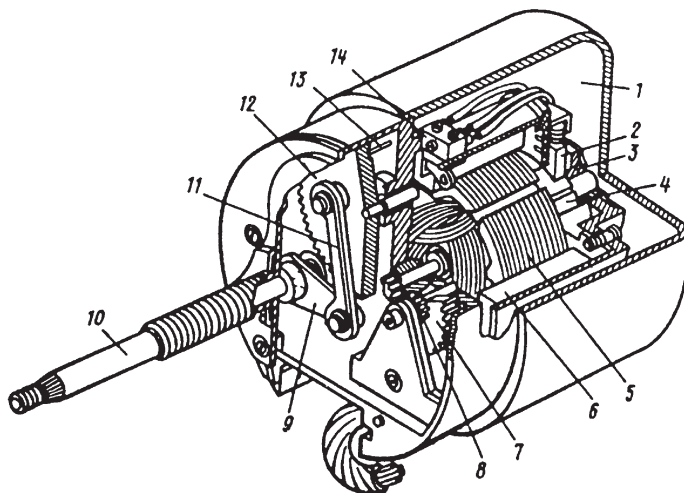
Малогабаритный моторредуктор 221.3730 фарочистителя:
